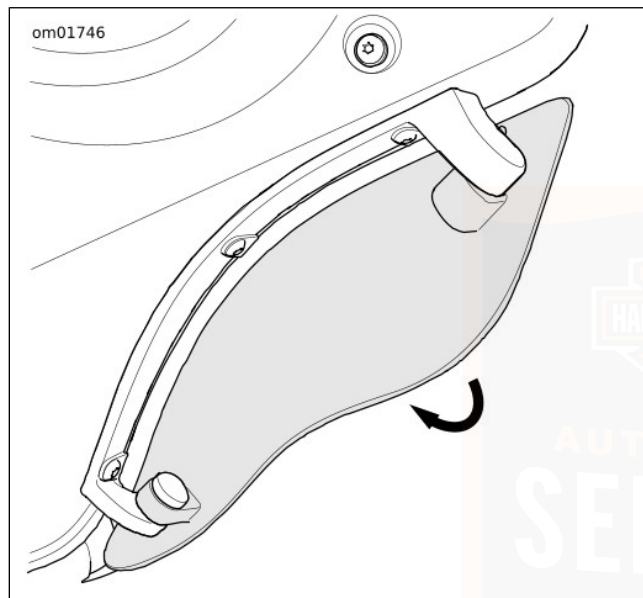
Splitstream ventilation i strømliniebeklædning
